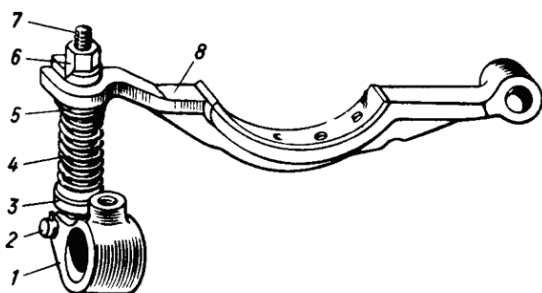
Разборка тормоза: 1 — серьга; 2 — палец; 3 — стакан; 4 — пружина; 5 — седло; 6 — гайка; 7 — болт; 8 — колодка
